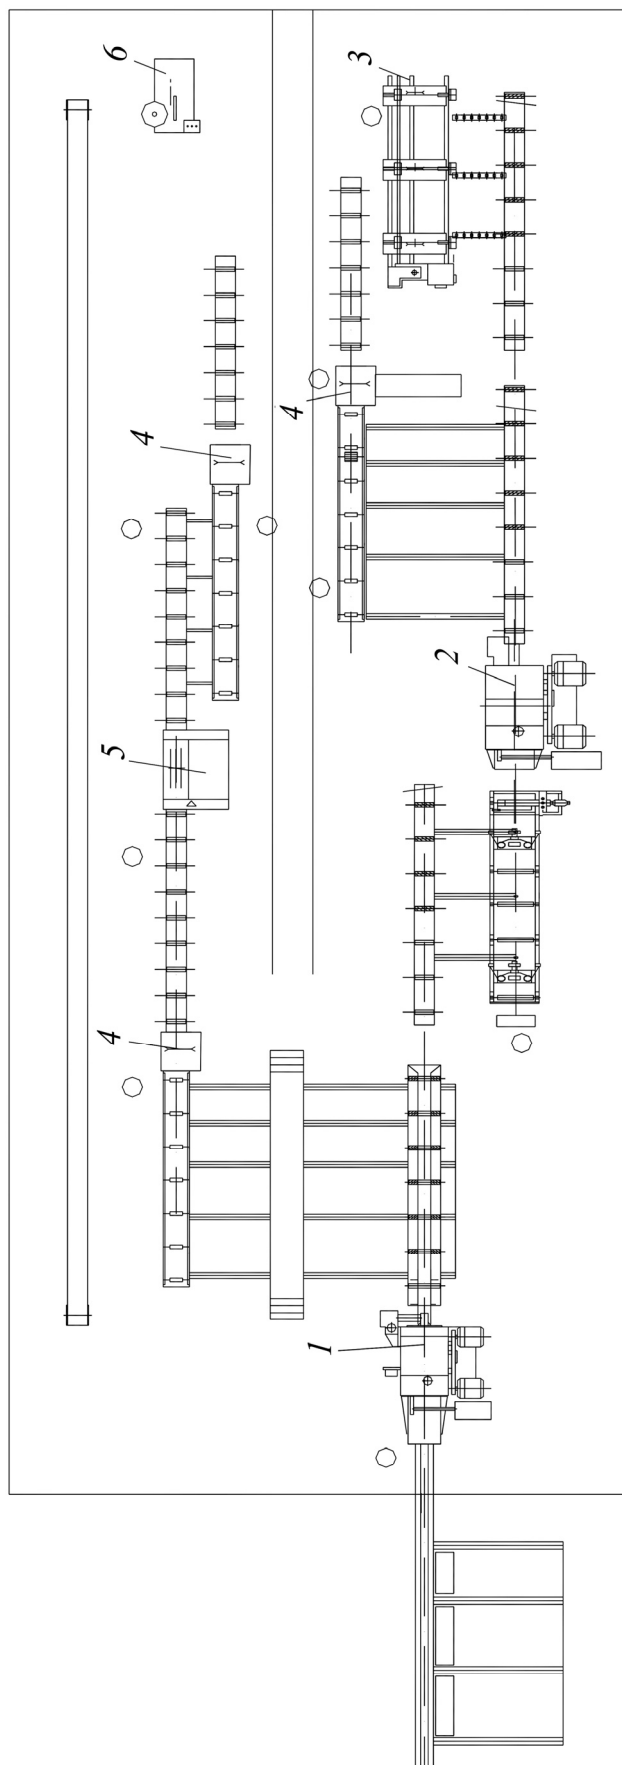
Схема расположения оборудования в цехе на базе многоопильных круглопильных станков:
